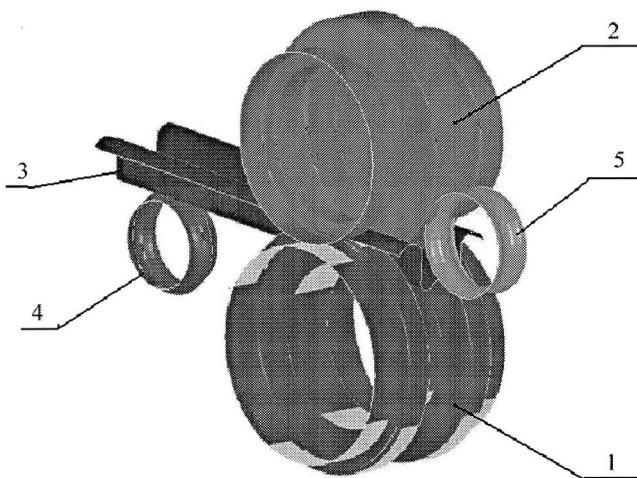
Твёрдотельная модель заготовки и роликов: 1 – нижний ролик; 2 – верхний ролик; 3 – заготовка; 4, 5 – направляющие
